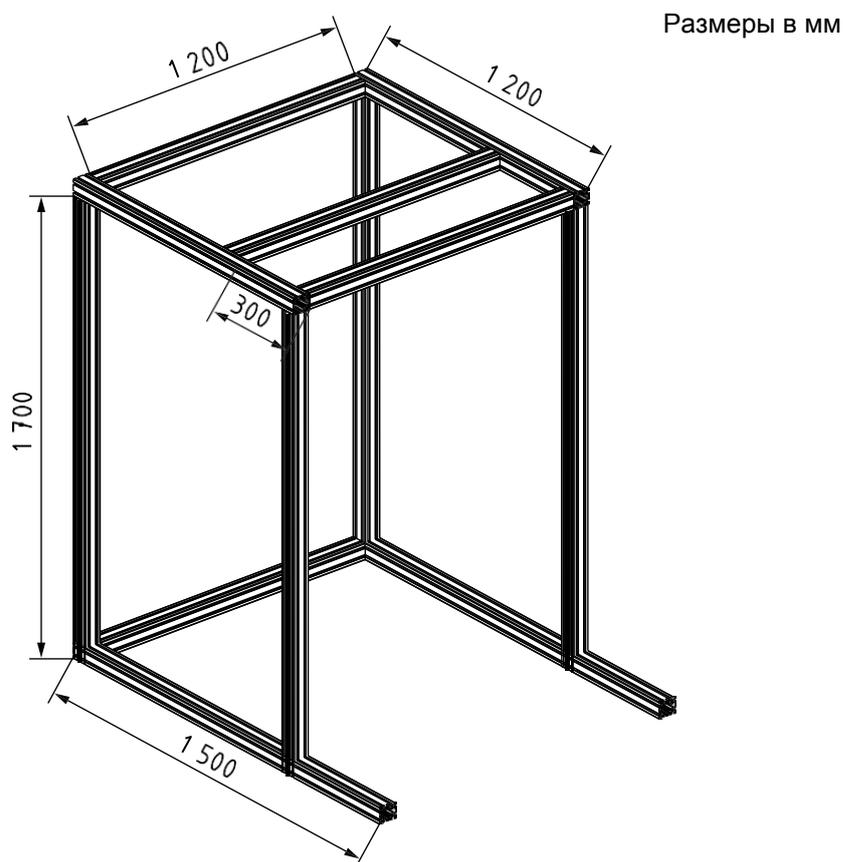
Пример конструкции и размеров каркаса испытательного оборудования
